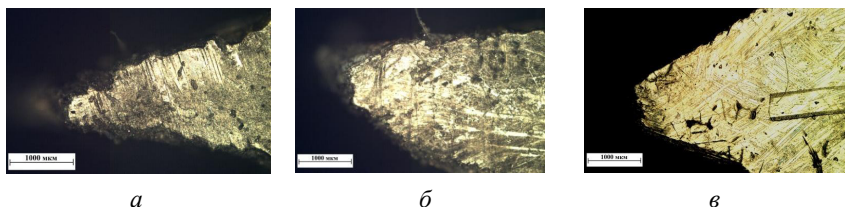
Углы криволинейного профиля после ПВЭЭО пакета ПКМ из трех заготовок с расположением токопроводящих слоев по краям заготовки
